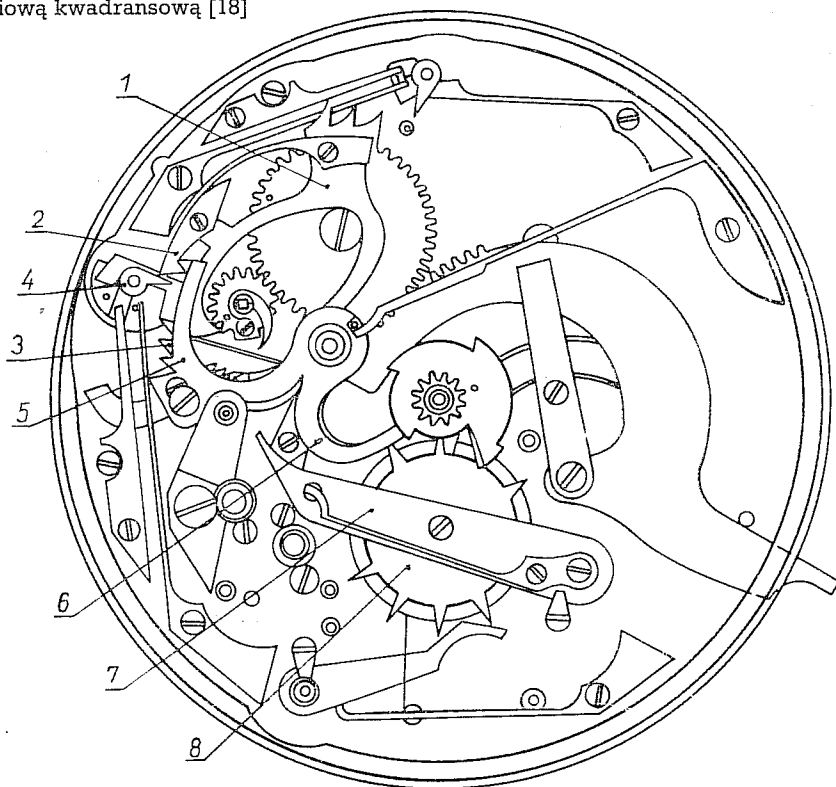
Mechanizm repeteria półkwadransowego [18]
